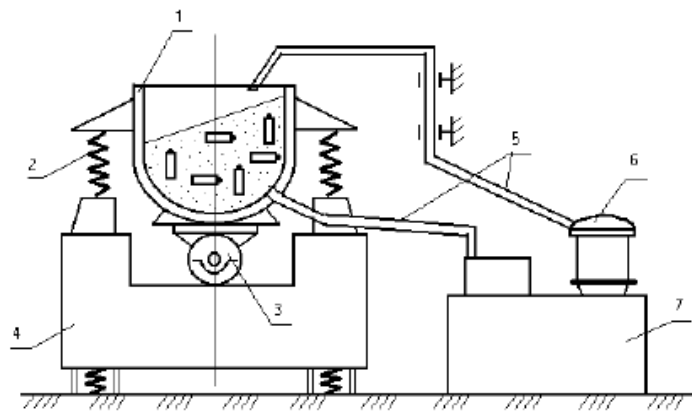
Схема процесса виброобработки: 1) рабочая камера станка; 2) пружины; 3) вибратор; 4) основание; 5) трубопроводы; 6) помпа; 7) бак-отстойник
